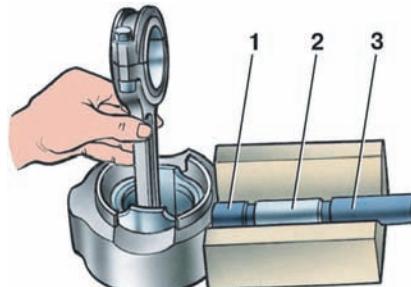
Пристосування для випресування і запресовки поршневого пальца: 1 – направлена; 2 – палець; 3 – плунжер
